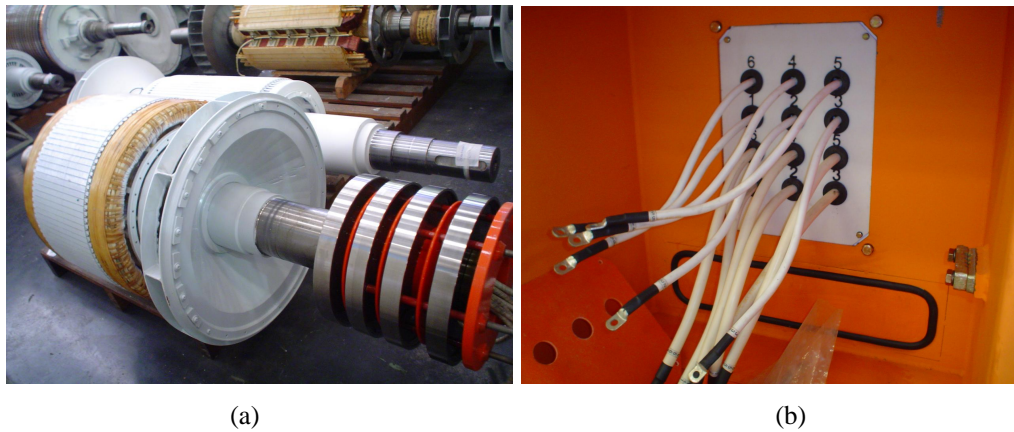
(a) Rotor bobinado com os anéis, (b) Cabos de ligação.
